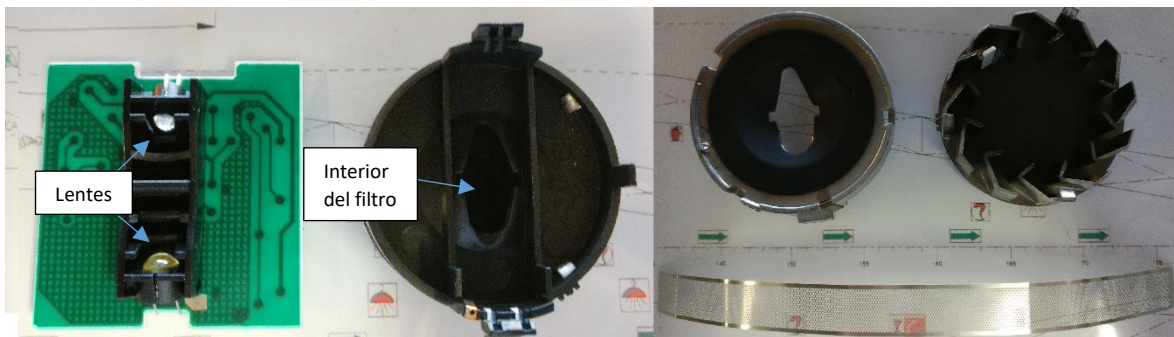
Chip con lentes + filtro (izqda.); despiece del filtro (drcha.). Fuente propia.
